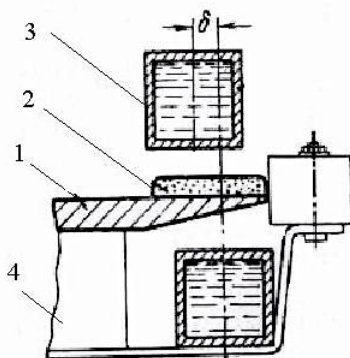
Схема расположения наплавляемой детали в индукторе:
